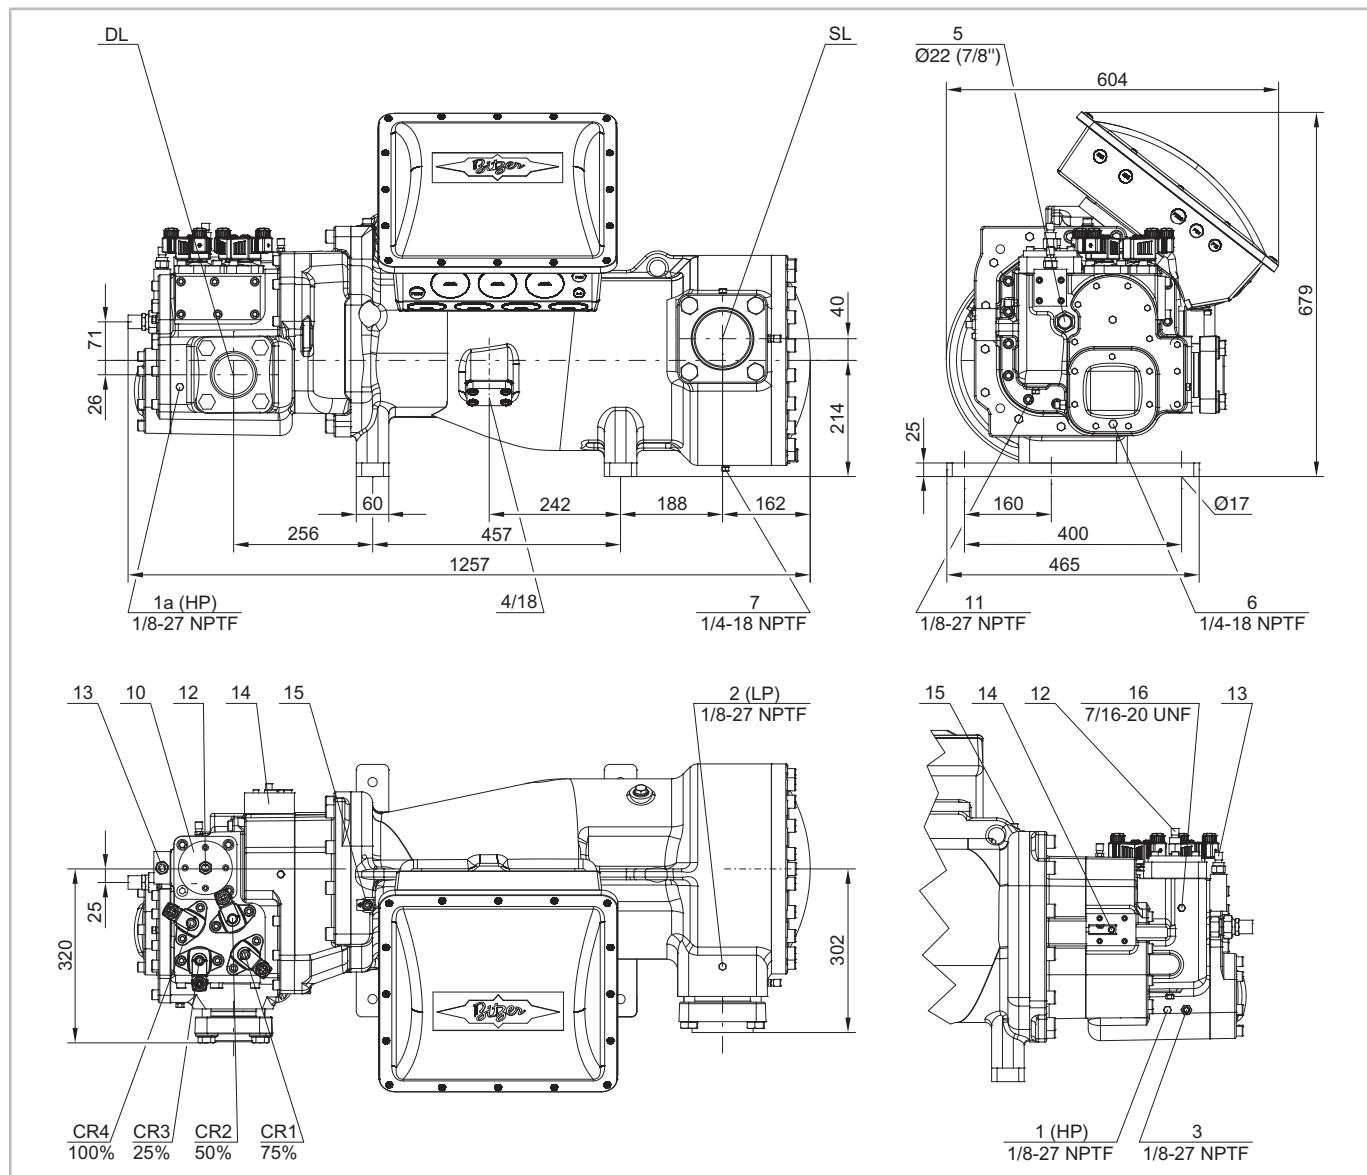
Maßzeichnung HS.8551 .. HS.8571
